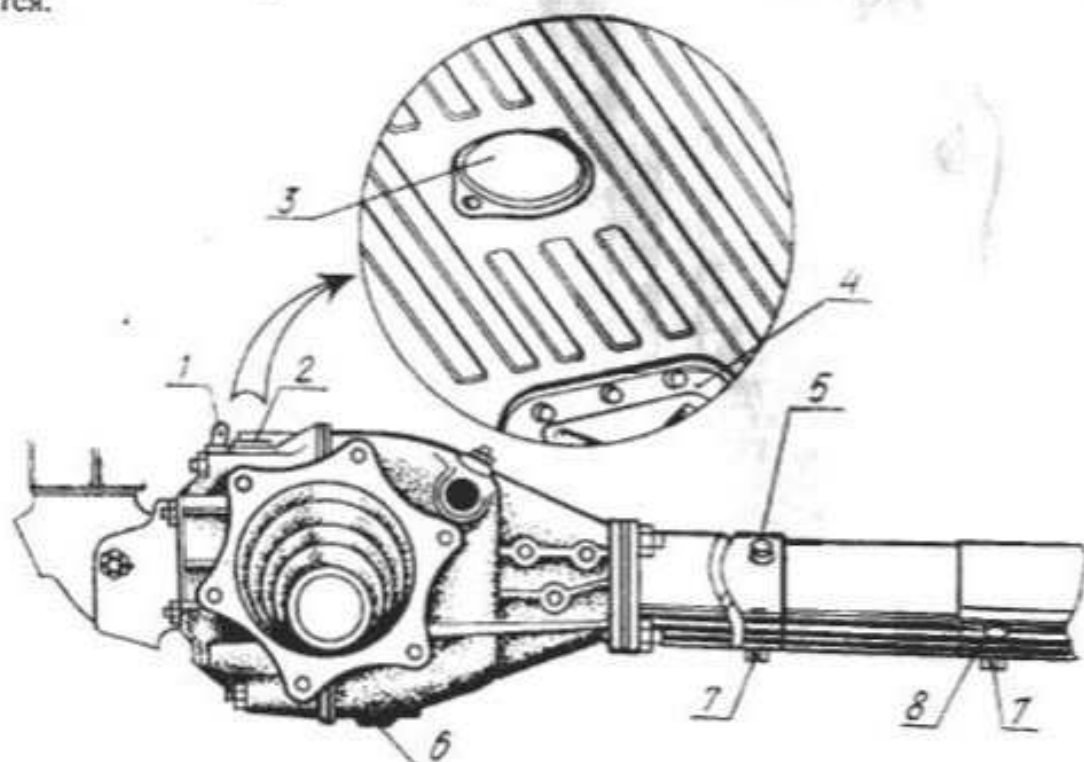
Кожух приводного вала, крышки и картер редуктора заднего моста:
